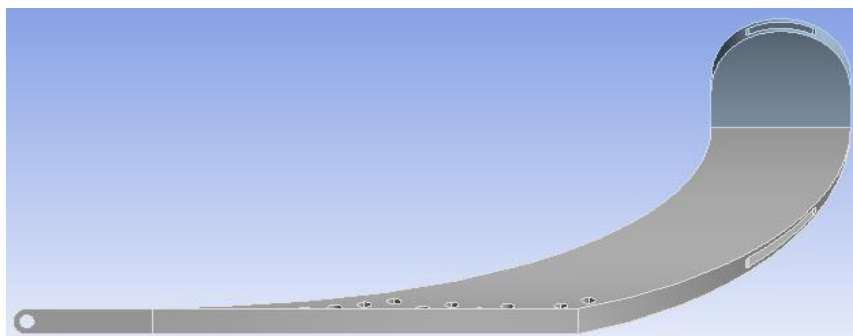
Diseño N°6 eslabón pierna izquierda, vista 4.
